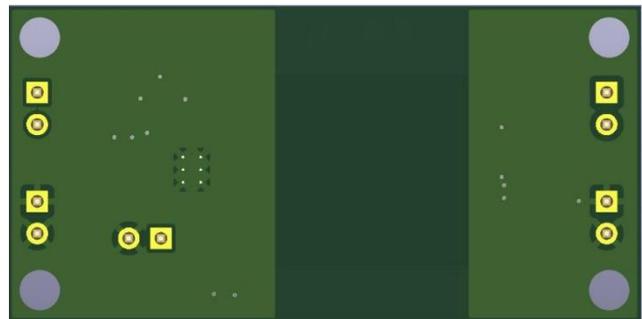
PCB 版图反面(尺寸: 25 x 50mm)
